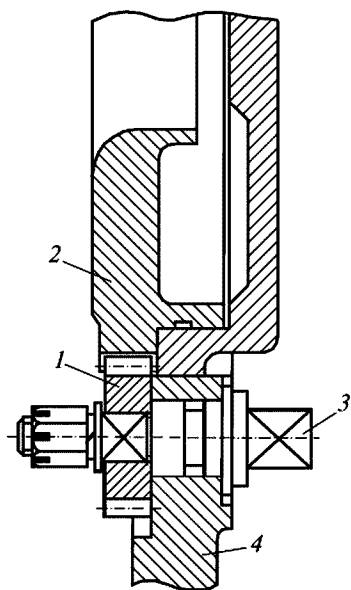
Поворотный механизм траверсы электродвигателя ДТК-800КЭ
